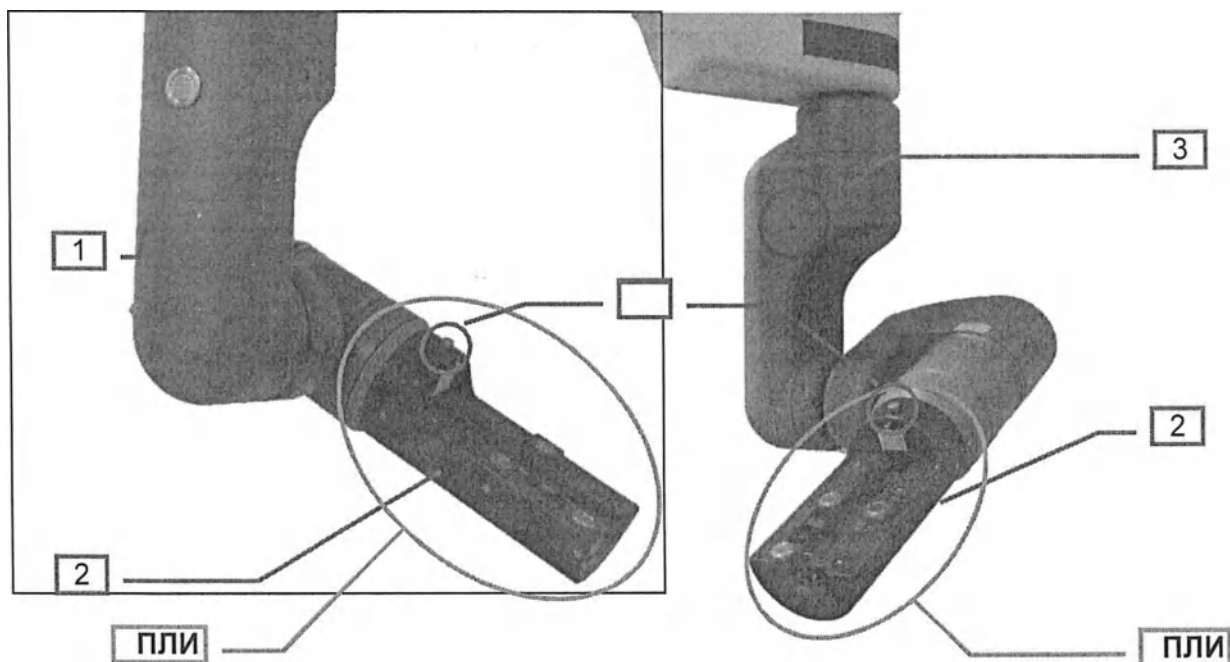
Стыковка ПЛИ и поворотные переключатели
